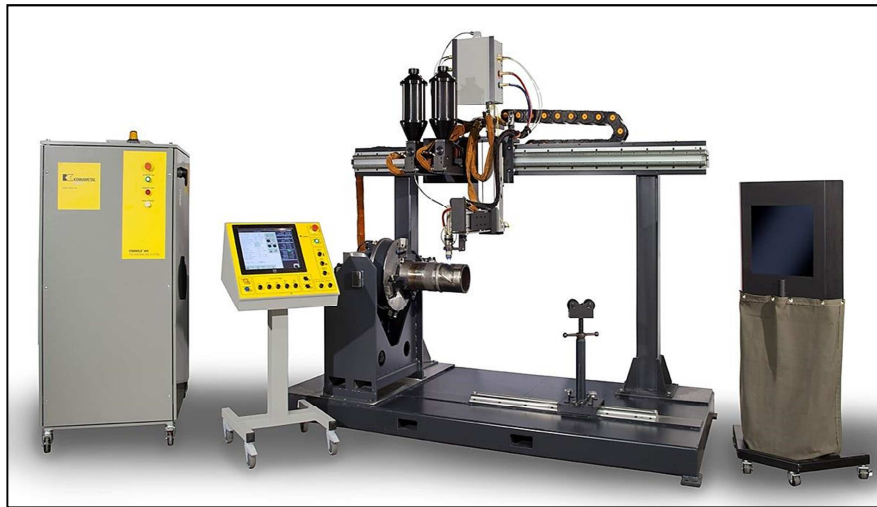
Equipamento de soldagem PTA Starweld 400 do fabricante Kennametal (Adaptado de Kennametal).
